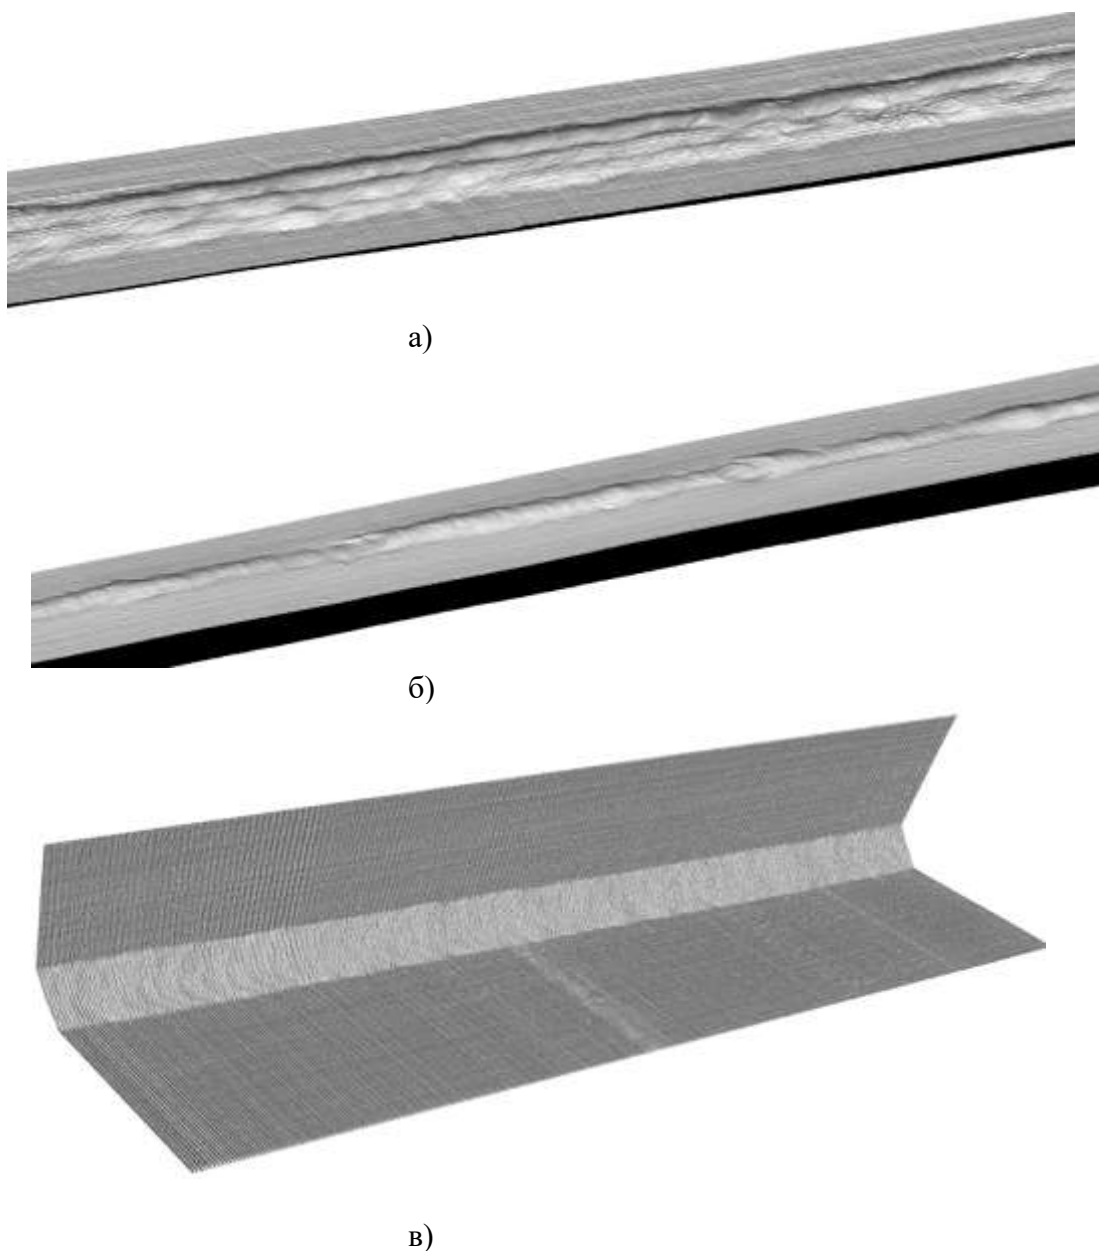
Визуализация цифровой реплики лицевой (а), корневой (б) поверхности стыкового сварного шва и лицевой (в) поверхности углового сварного шва КСС.
